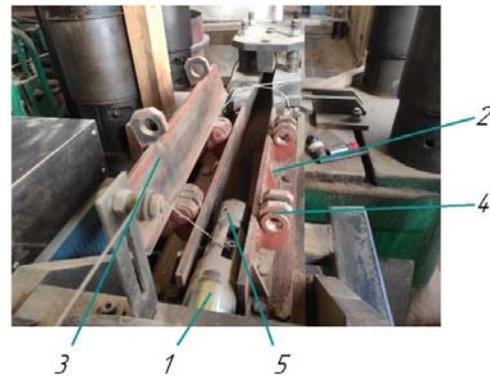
Механотронный модуль прессования брикетов: 1 – электроцилиндр; 2 – пресс-форма; 3 – крышка прессформы, 4 – механизм фиксации крышки с пресс-формой; 5 – пуансон
